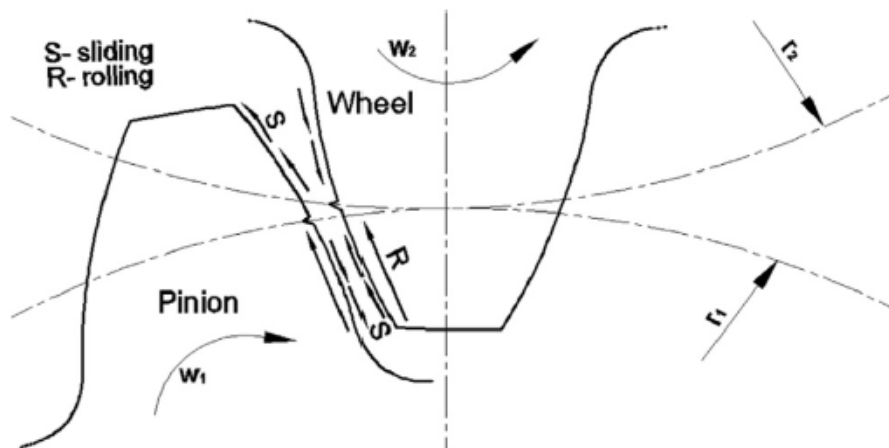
Ilustração do movimento relativo na superfície do dente de uma engrenagem [65].
